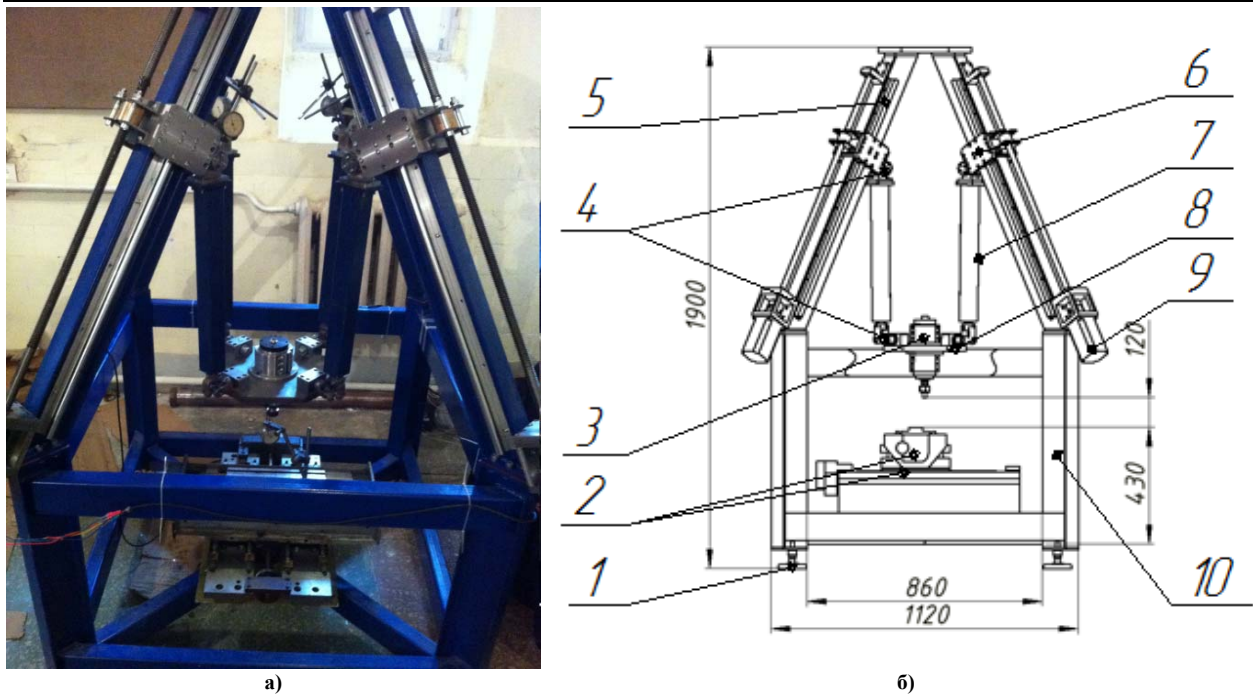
Свердильно-фрезерний верстат пірамідальної компоновки: а – фото зі встановленими індикаторами; б – загальний вид – опора 1, хрестовий стіл 2, мотор-шпиндель 3, шарнір 4, напрямна 5, каретка 6, штанга постійної довжини 7, рухома платформа 8, лінійний двигун 9, каркас 10.
